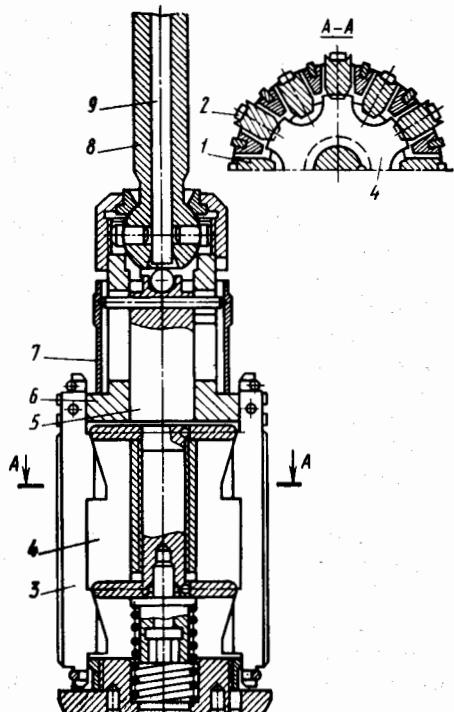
Приспособление для запрессовки гильзы в блок цилиндров
